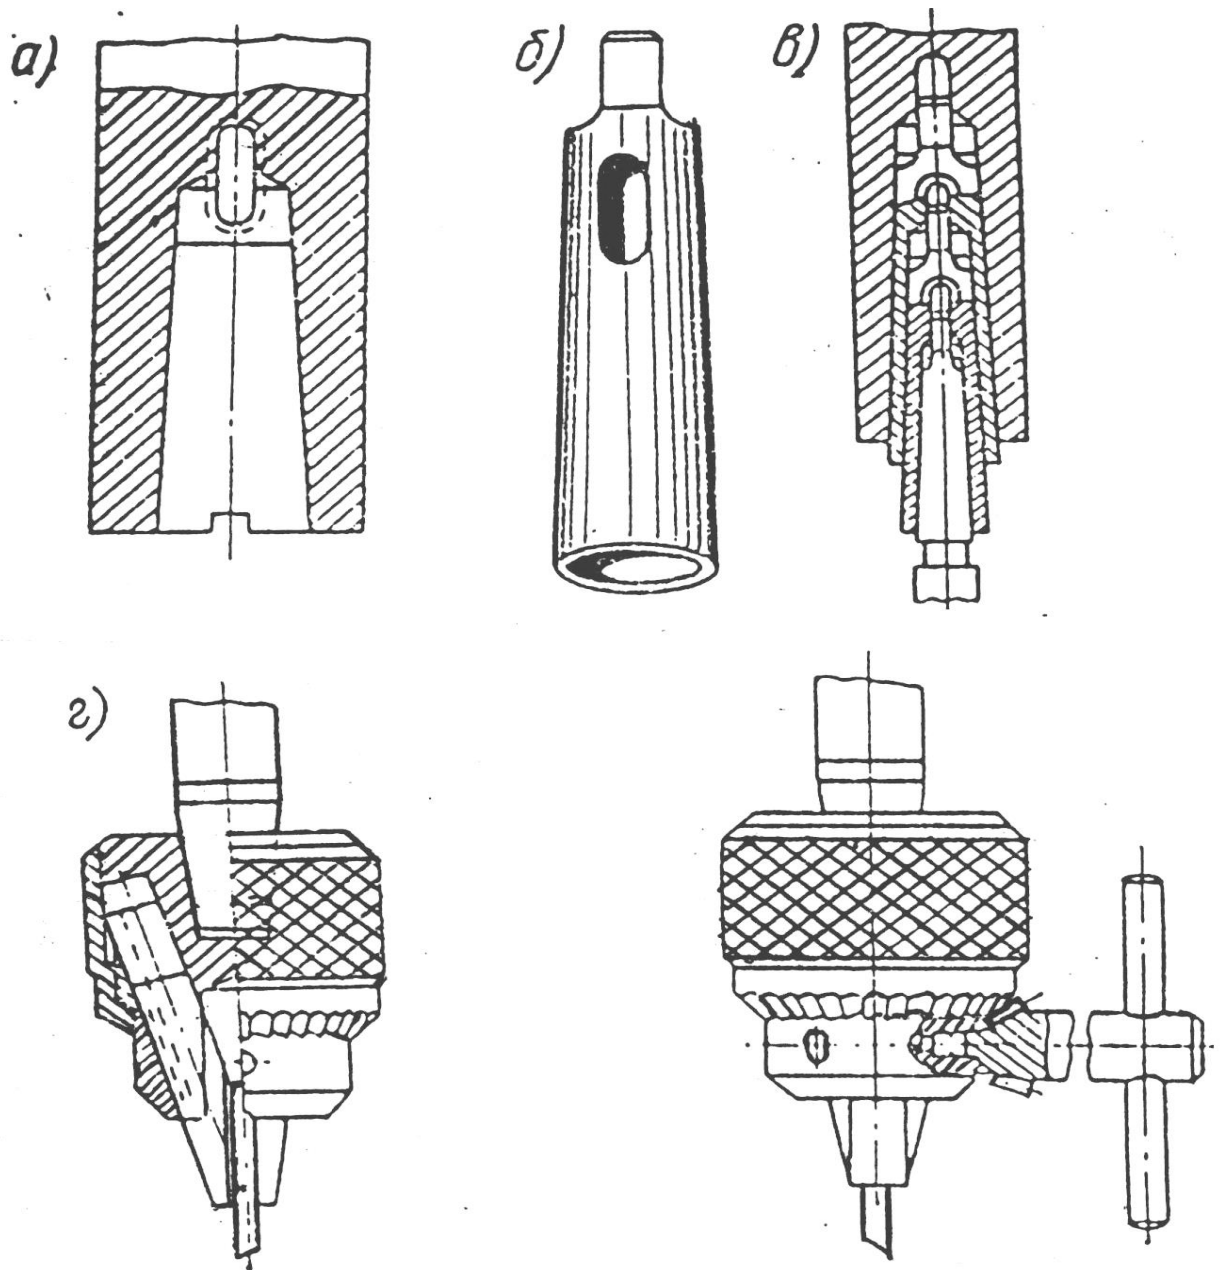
2 – Вспомогательные инструменты для сверления отверстий:
